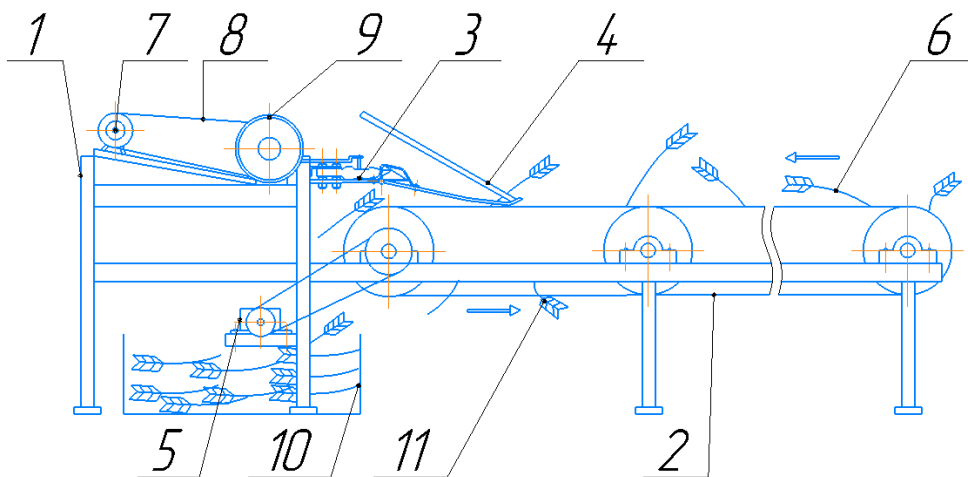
Лабораторная установка: 1 – рама; 2 – ленточный транспортёр; 3 – режущий аппарат; 4 – копирующий стеблеподъемник; 5 – мотор-редуктор; 6 – стебли зерновой культуры; 7 – электродвигатель; 8 – клиноременная передача; 9 – механизм качающейся шайбы; 10 – ящик-сборник; 11 – срезанные стебли.
